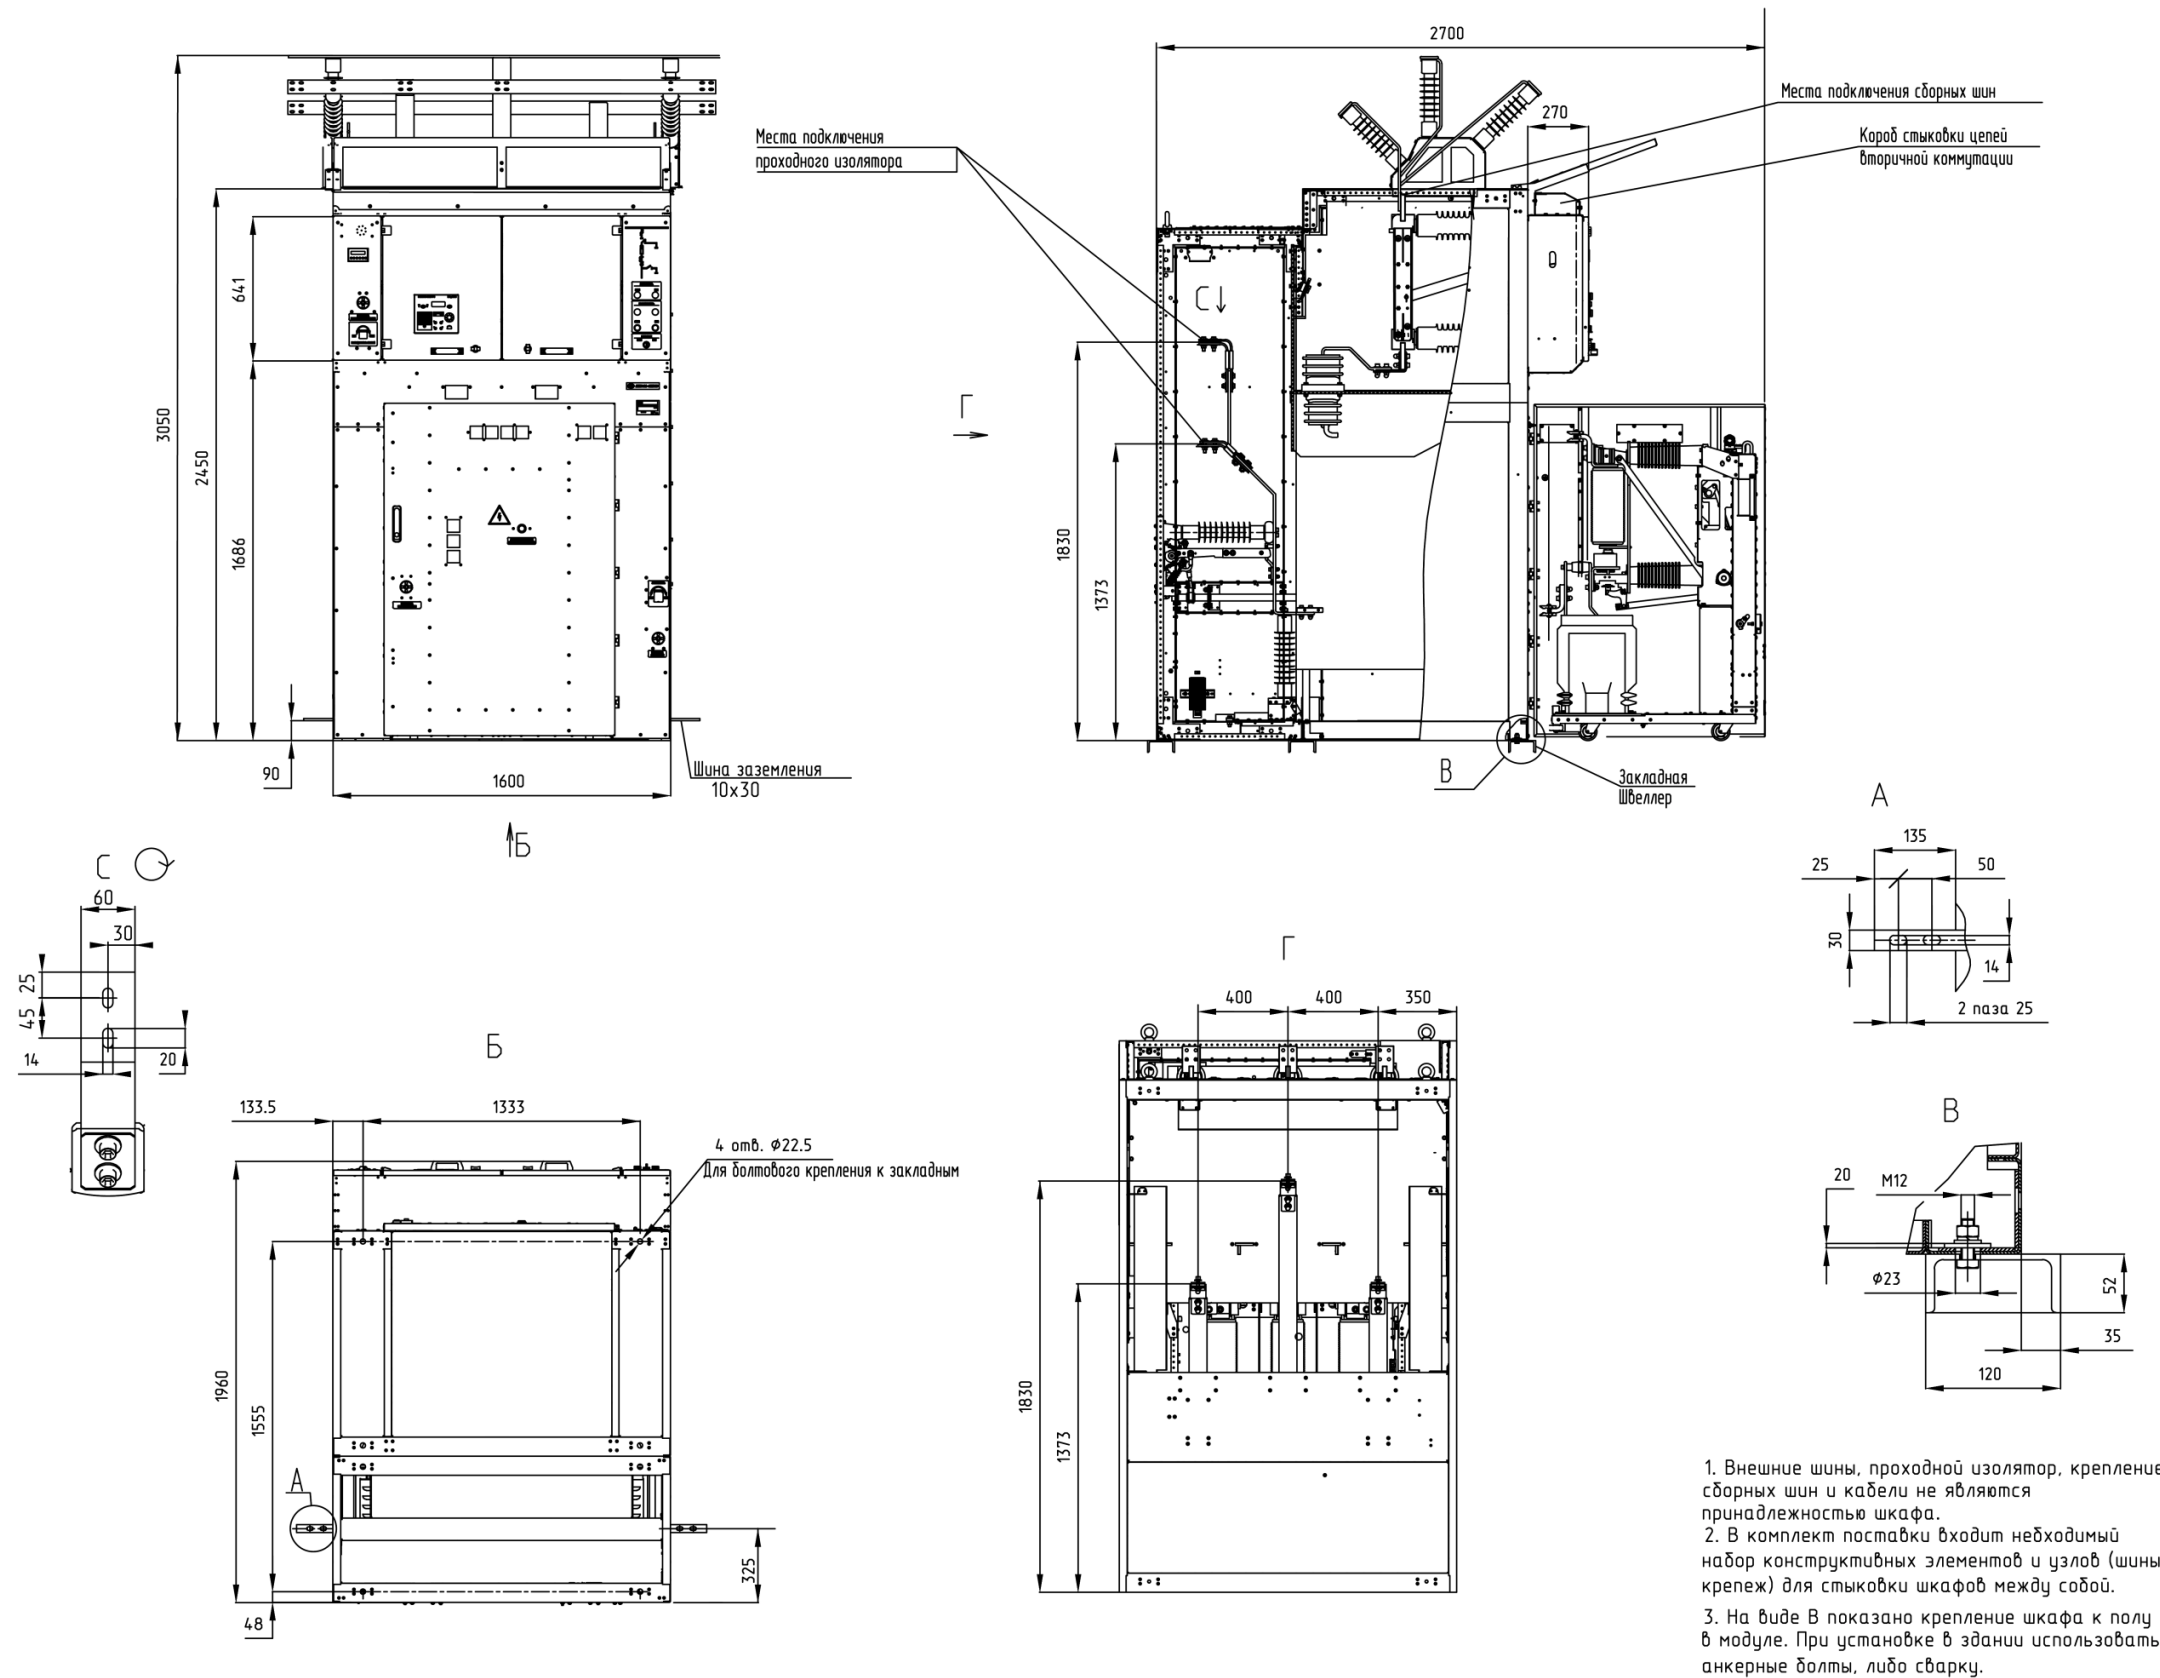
Шкафы с шинным подключением: Шкаф выключателя ввода 1С-35-3-ВВ-УХЛ4 номер схемы 01; шкаф фидера 1С-35-3-Ф-УХЛ4 номер схемы 02; шкаф выключателя ПВА 1С-35-3-ПВА-УХЛ4 номер схемы 03; шкаф выключателя ТСН 1С-35-3-ТСН-УХЛ4 номер схемы 04, масса – не более 1750 кг.
